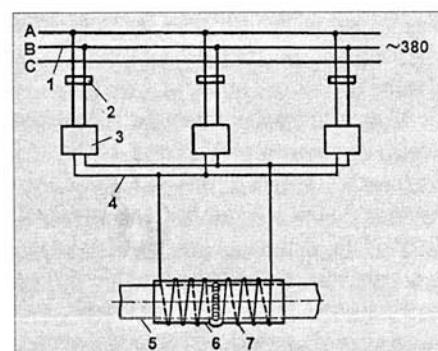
Схема параллельного соединения сварочных трансформаторов для индукционного нагрева: 1 — трехфазная электрическая сеть переменного тока напряжением 380 В; 2 — контакторы; 3 — сварочные трансформаторы; 4 — провода для соединения индуктора с трансформатором; 5 — сварное соединение трубы; 6 — теплоизоляция; 7 — индуктор
